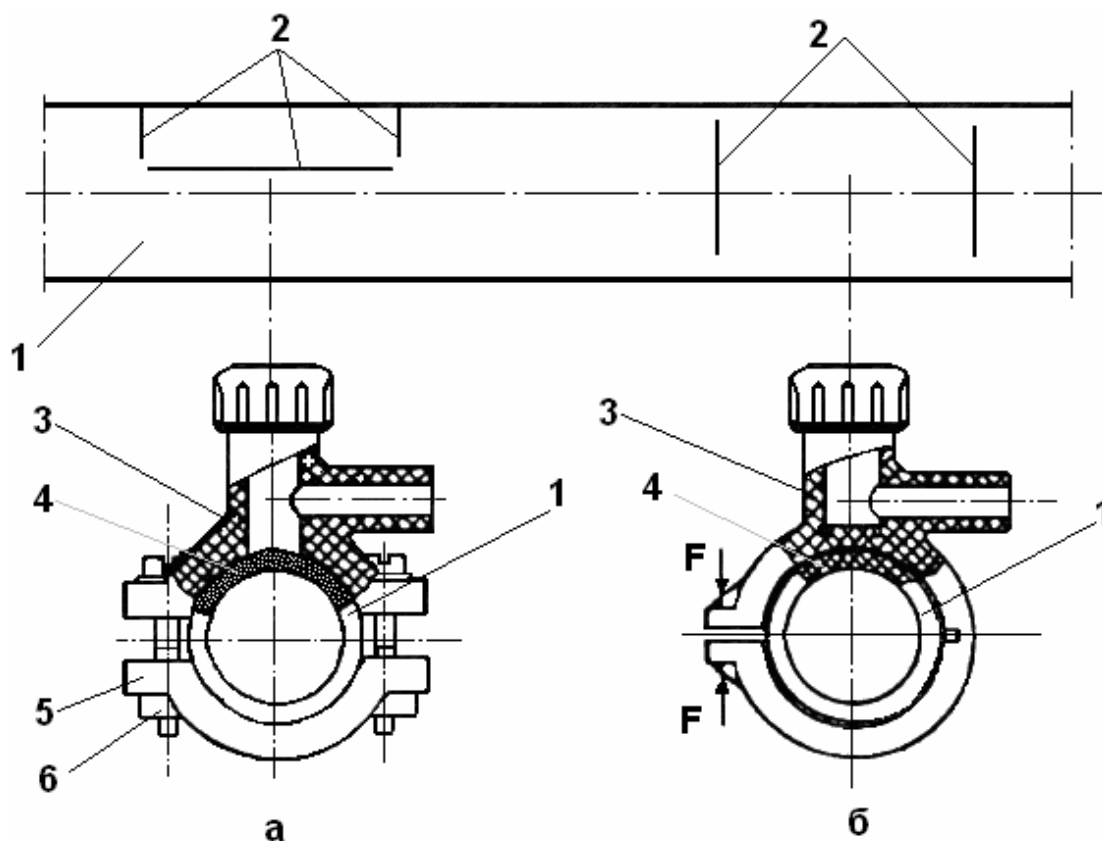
Схема сварки седловых отводов с закладными нагревателями с трубой
